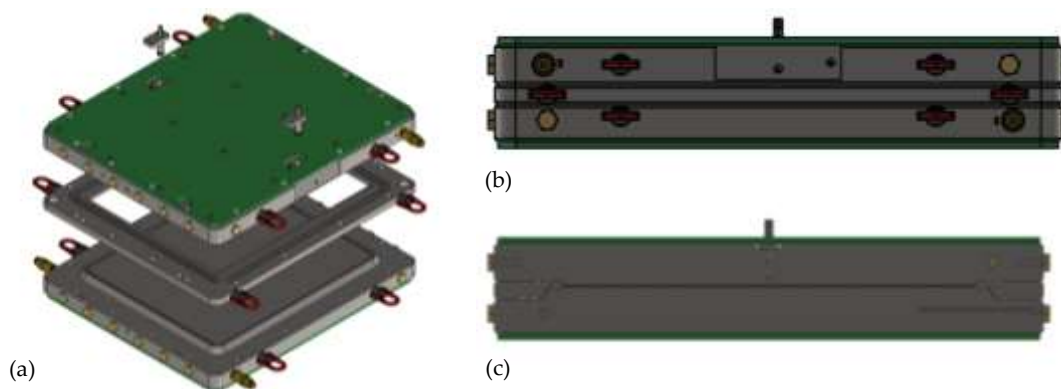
Molde de placa plana para el proceso de transferencia de resina o infusión: (a) vista del explosionado del molde, (b) vista de perfil del molde cerrado y (c) vista de la sección transversal del molde (condición: cavidad del molde cerrada).
